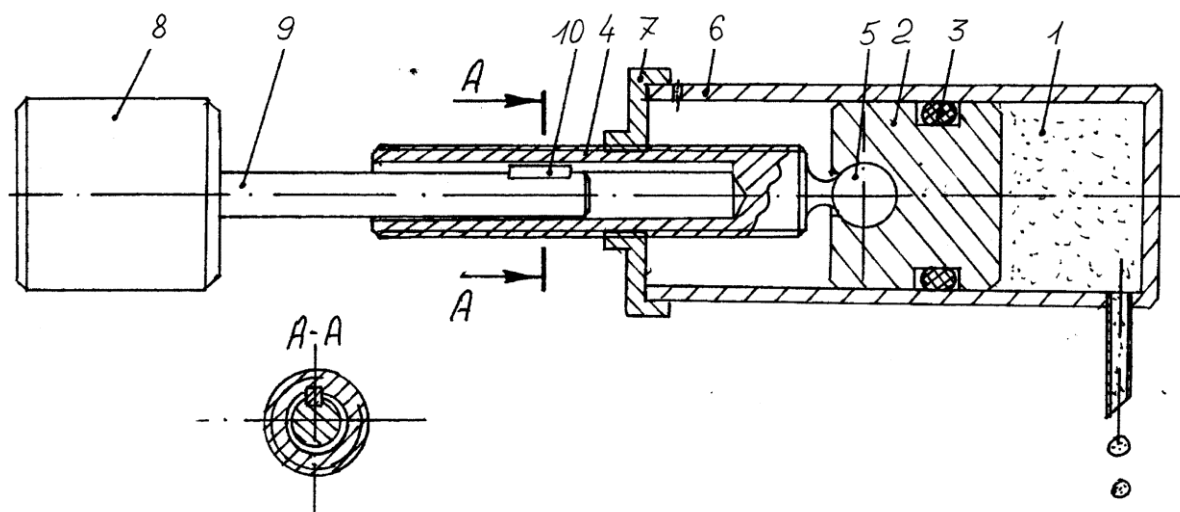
Конструкція дозатора присадок 1 – ємкість для присадки; 2 – поршень; 3 – ущільнююче кільце; 4 – мікрометричний гвинт; 5 – кулька; 6 – кришка; 7 – гвинту з мікрометричною різьбою; 8 – кроковий електродвигун; 9 – вал; 10 – шпонка, яка передає кутовий момент мікрометричному гвинту
